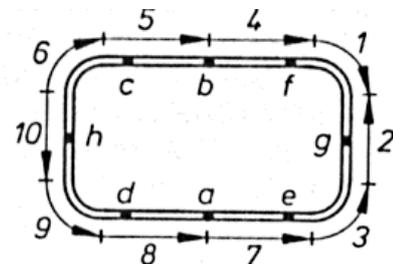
Heft- und Schweißfolge; Heftfolge a-h, Schweißfolge 1-10, /1/
